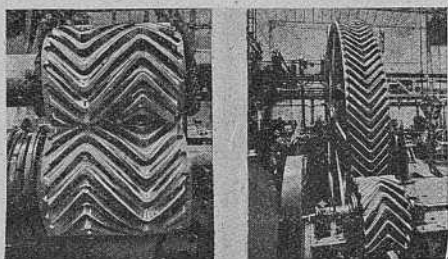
Engranajes helicoidales de doble y triple espiral.
